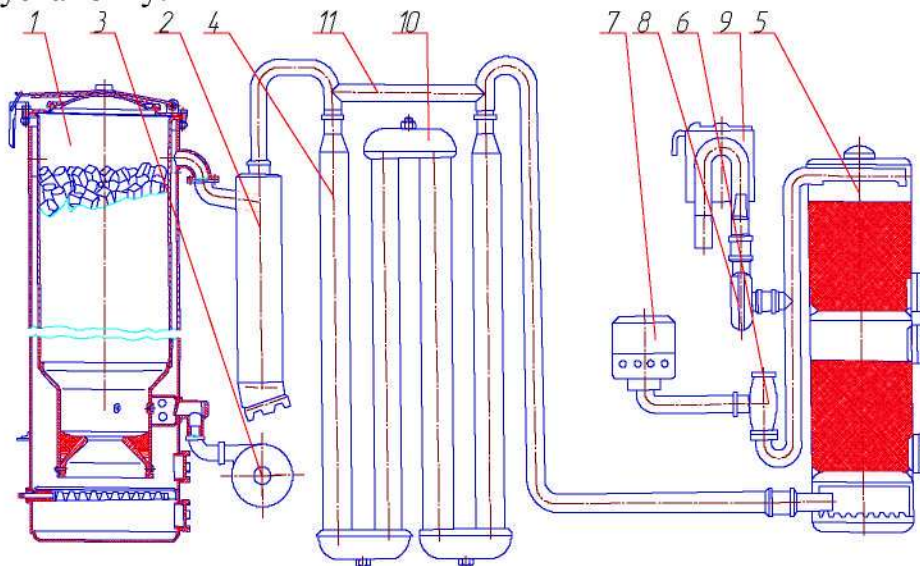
Схема газогенераторної установки: 1 - газогенератор; 2 – грубий інерційний очисник газу; 3 - електровентильатор для запалювання (повіродувка); 4 – охолоджувач; 5 - газоповітряний фільтр – змішувач; 6 – вертикальний тонкий очищувач; 7 – повітроочищувач; 8 – вентилятор; 9 – пусковий підігрівач; 10 – кришка; 11 – перепускна труба.
